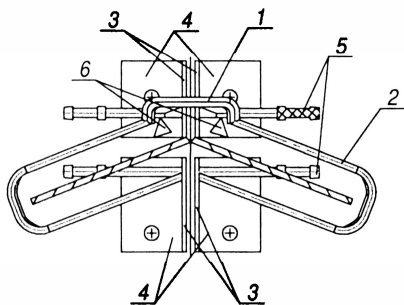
Индуктор для одновременной наплавки носовой части стрелчатой лапы и закалки ее крыльев:
